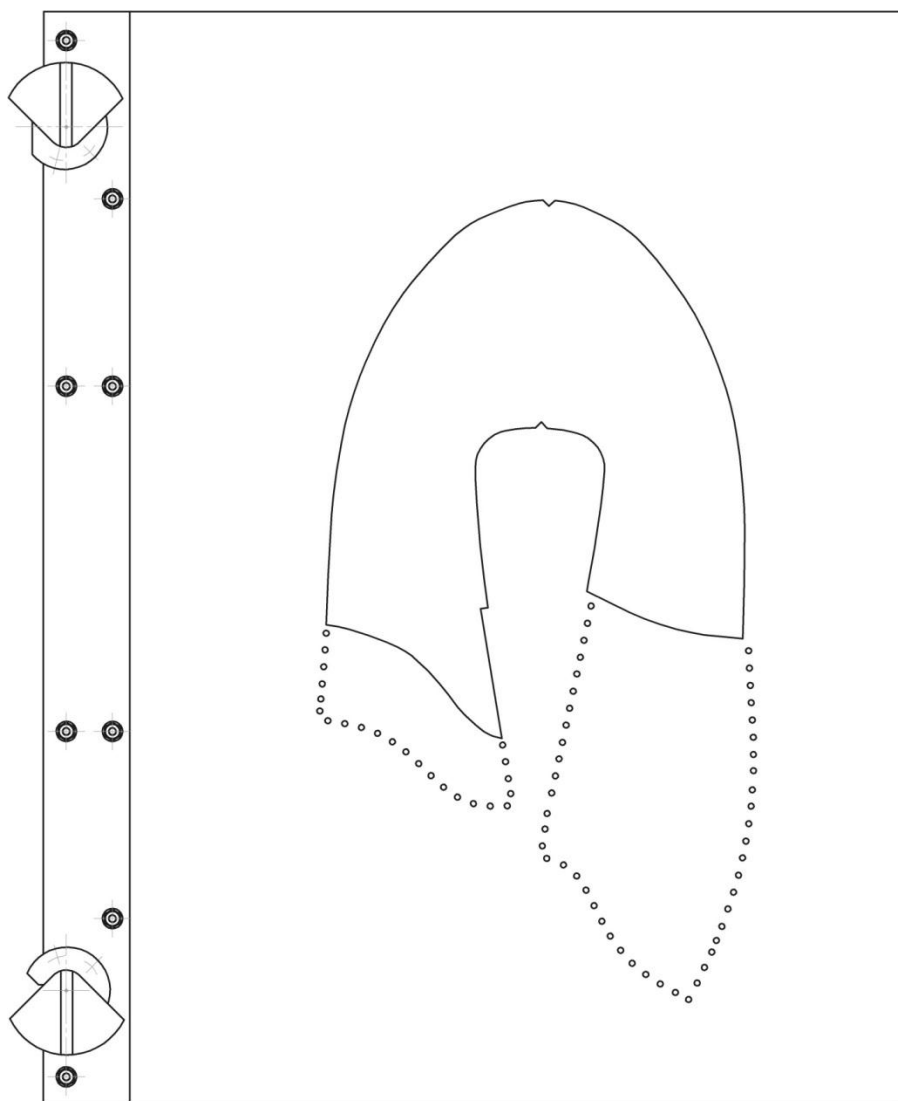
Конструкция кассеты для сборки заготовки верха обуви
